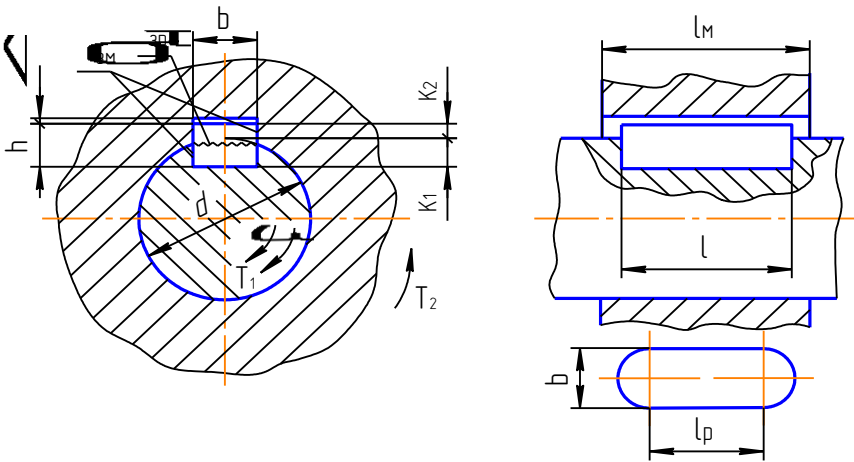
Конструкція шпонкового з'єднання з призматичною шпонкою
